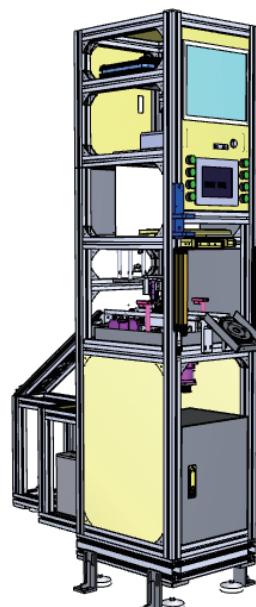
齿轮焊缝检测系统 3D 结构示意图
